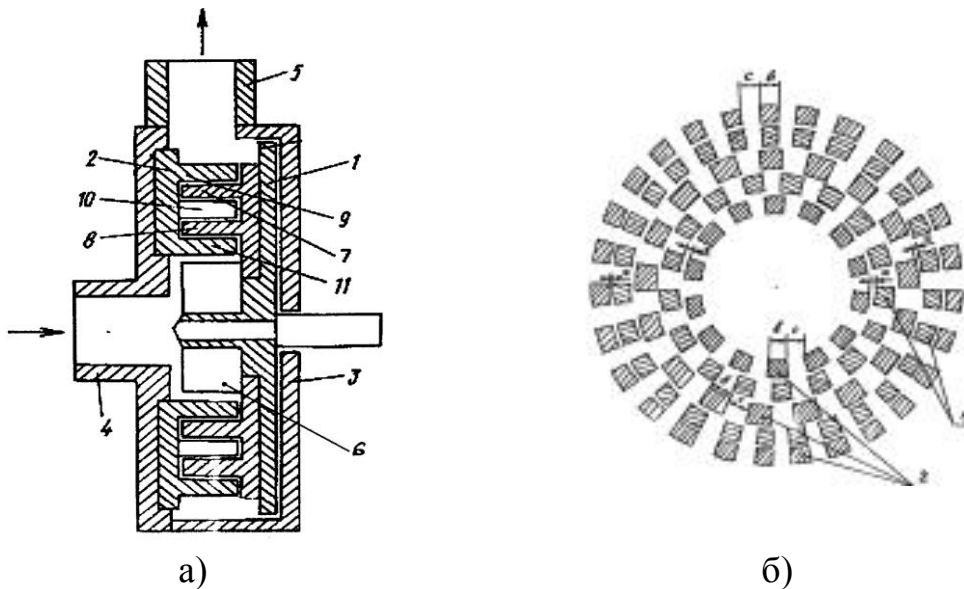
Роторно-пульсационный аппарат: а-вид сбоку; б-вид сверху. Цифрами обозначены 1-корпус; 2-входной патрубок; 3-выходной патрубок; 4-статор; 5- коаксиальные цилиндры; 6- проточные каналы; 7-вал; 8-ротор; 9- коаксиальные цилиндры; 10- проточные каналы; 11- безканальный дискообразный обод
